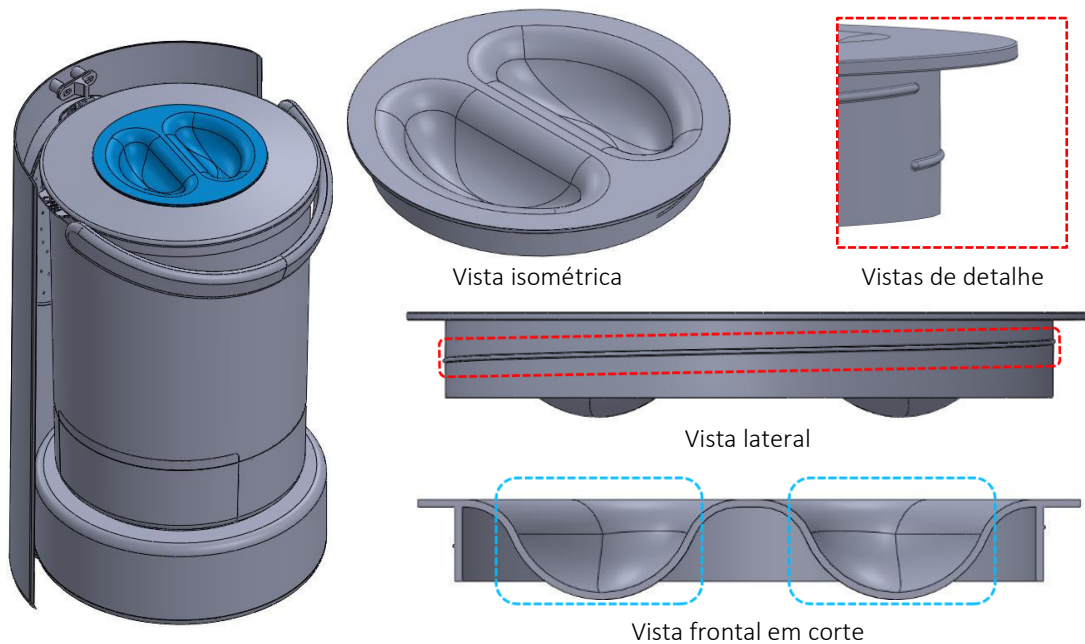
Sinalização de detalhes diversos da peça tampa pequena – módulo de compostagem (8).
